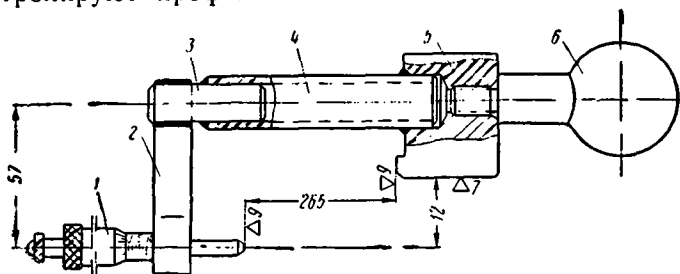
Микрометрическая скоба для контроля размера 265 на буксах моторно-осевых подшипников тяговых двигателей НБ-406 и НБ-412:
